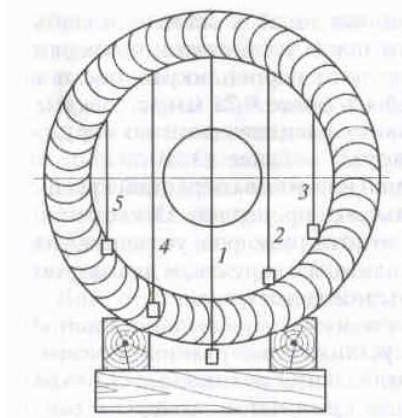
Проверка торцевого и радиального биения крыльчатки
